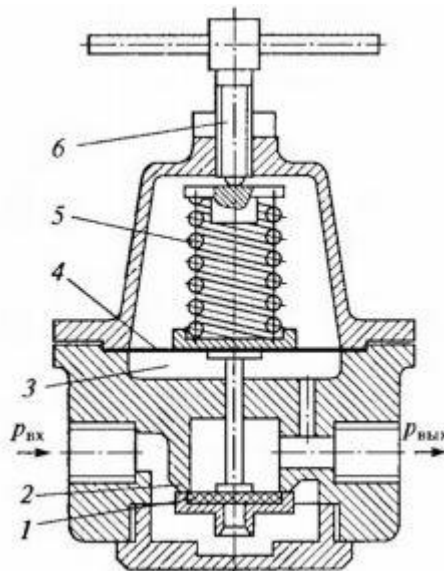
Пневматический редукционный клапан: 1 - запорно-регулирующий элемент; 2 - корпус; 3 - полость; 4 - мембрана; 5 - пружина; 6 - регулировочный винт.
